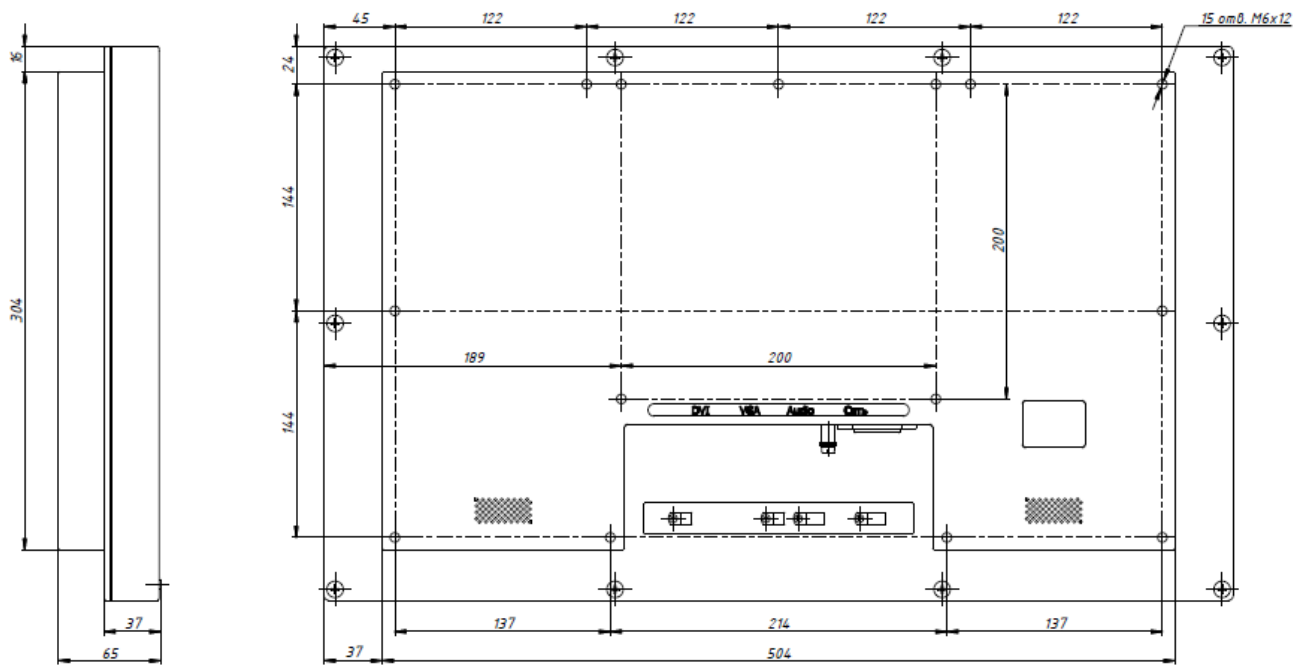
Габаритный чертёж видеомонитора в исполнении ВМП1225-АД-5-Х-Х-Х, вид сбоку и сзади, положения отверстий для крепления в щите и крепления VESA
